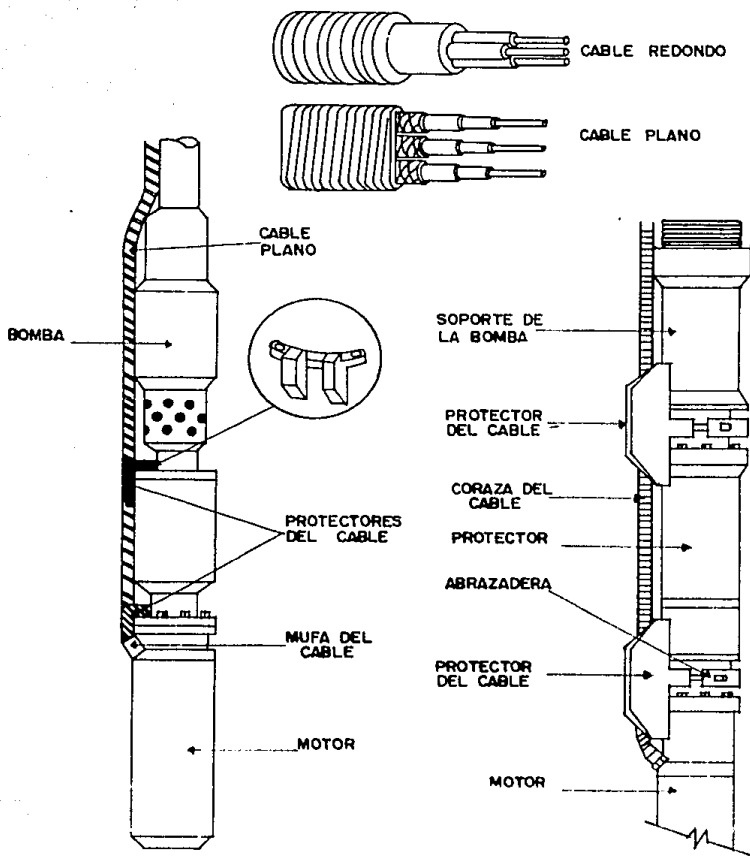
INSTALACION DE CABLES REDONDO Y PLANO.
